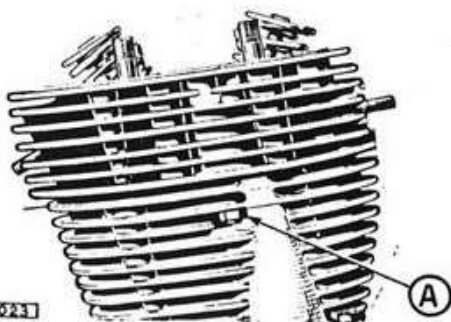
Dado (A) del prigioniero di fissaggio della testa dal lato sinistro
